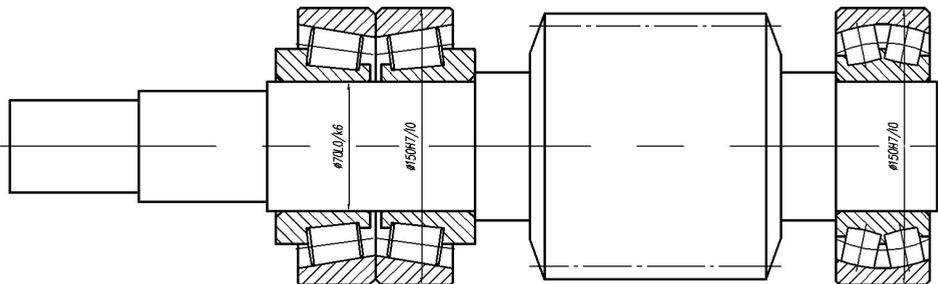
Установка червяка на фиксированной и плавающей опорах
